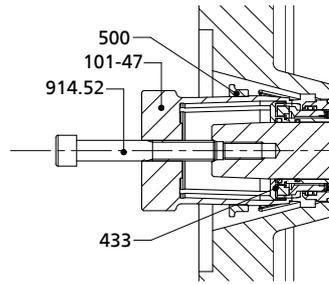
Desmontaje del cierre mecánico de cartucho doble C022/025/11-4STQ
